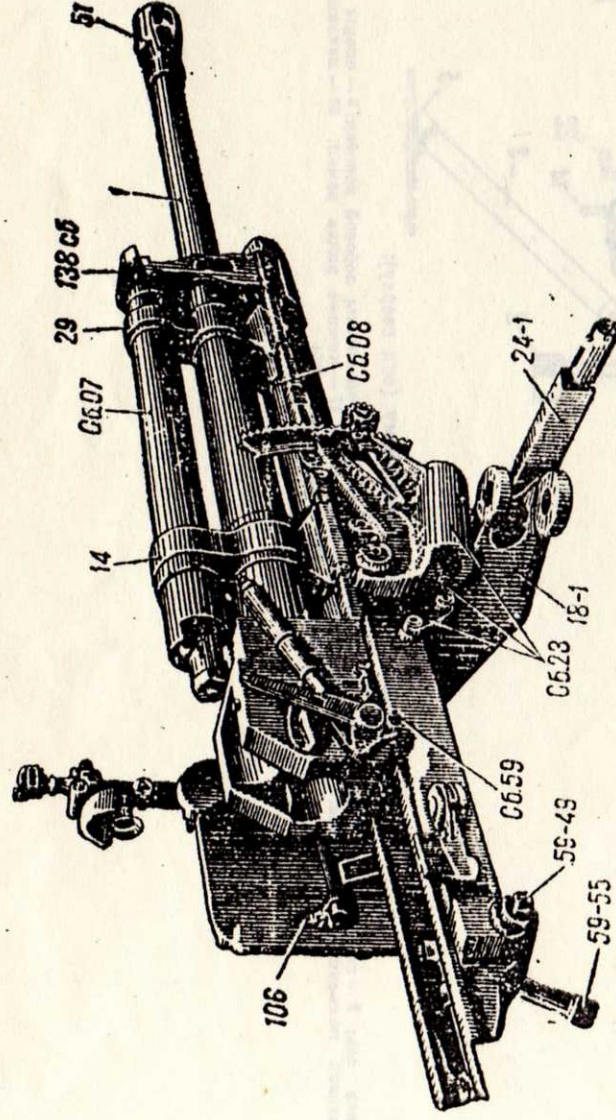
Вращающаяся часть пушки с лобовой коробкой и боевой осью (вид справа) (сб. 01):
